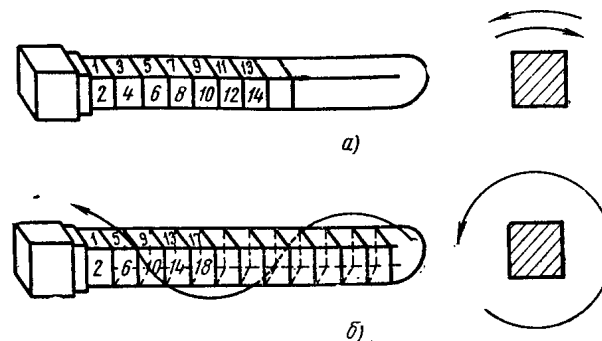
Схема способов вытяжки: а — при ковке крупных заготовок и слитков, б — при ковке инструментальных сталей
